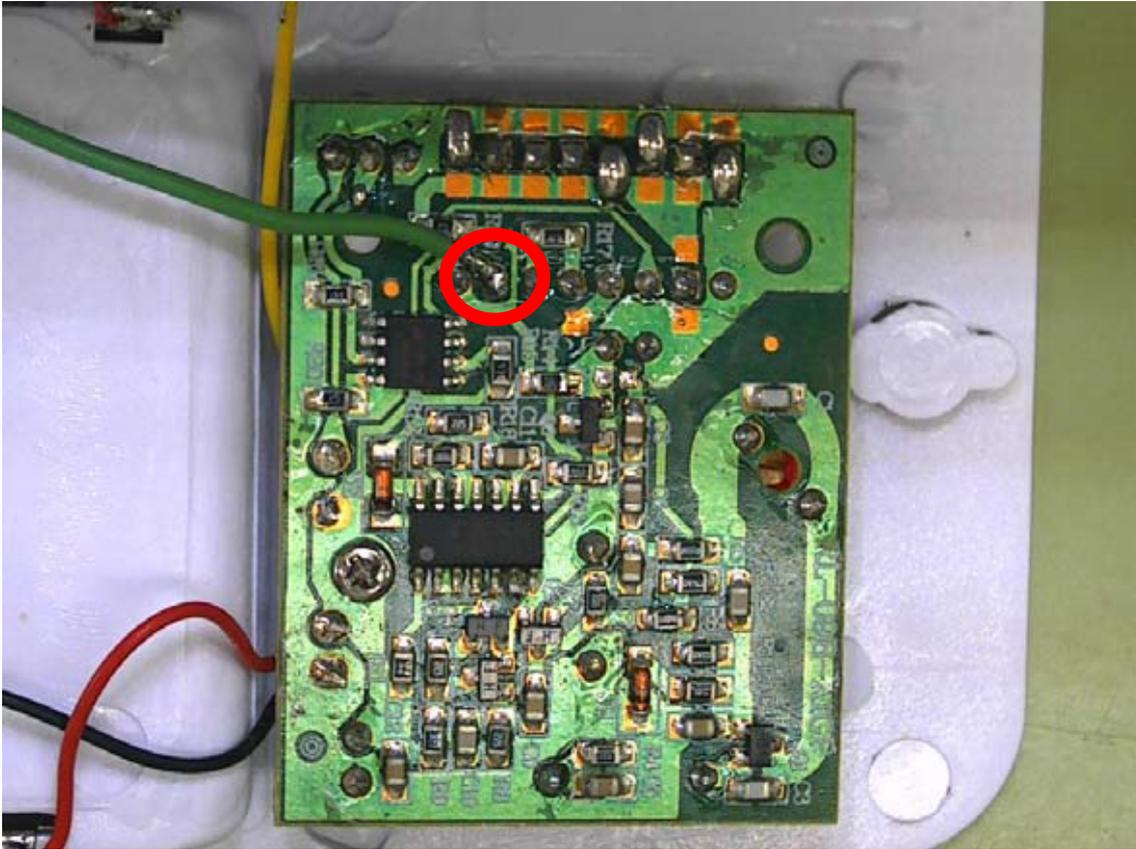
FOTO DE LA ADAPTACIÓN DEL TIMBRE EN LA CONEXIÓN DE LAS PILAS
